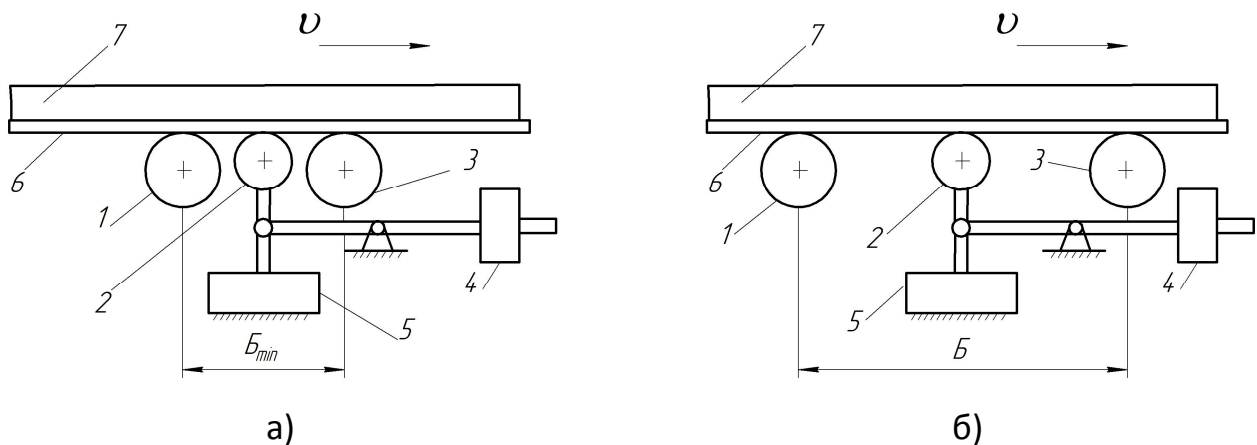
Положення несучих і опорного ролика при мінімальній (а) і збільшеній базі (б): 1, 3 – несучі роликки; 2 – опорний ролик; 4 – противага; 5 – перетворювач тиску матеріалу; 6 – конвеєрна стрічка; 7 – сипкий матеріал;  $B$  – базова відстань між несучими роликками;  $v$  – швидкість і напрям руху
